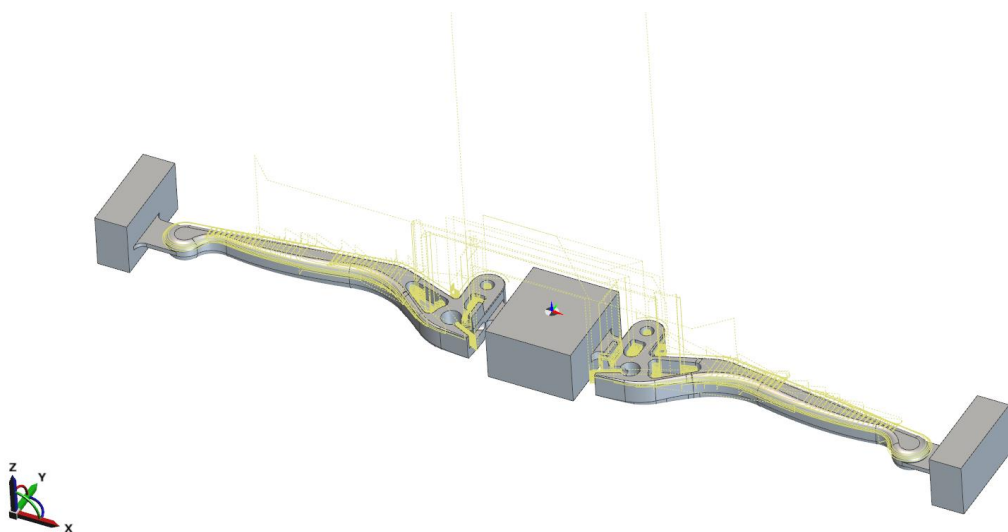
Dráhy nástroje příkazu „hrubování“ ve druhém upnutí
